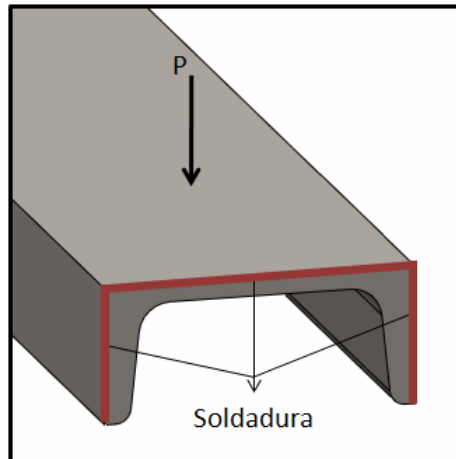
Cargas actuantes en la soldadura [Fuente: propio].
